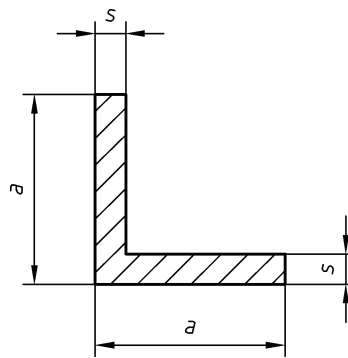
Warmgewalzter gleichschenkliger scharfkantiger Winkelstahl
